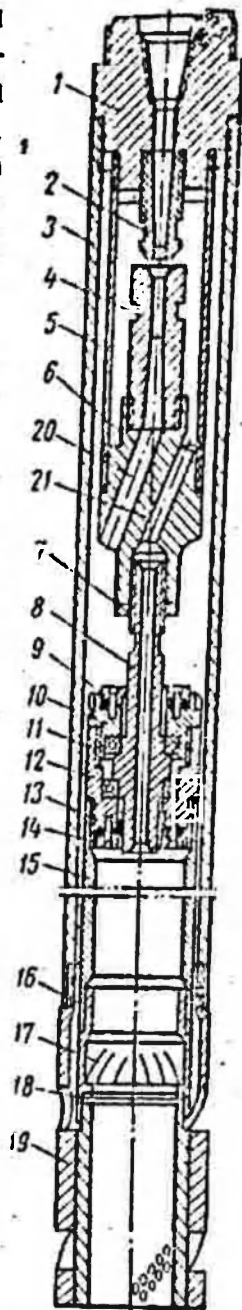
Двойной водоструйный колонковый снаряд конструкции КазНИМС
